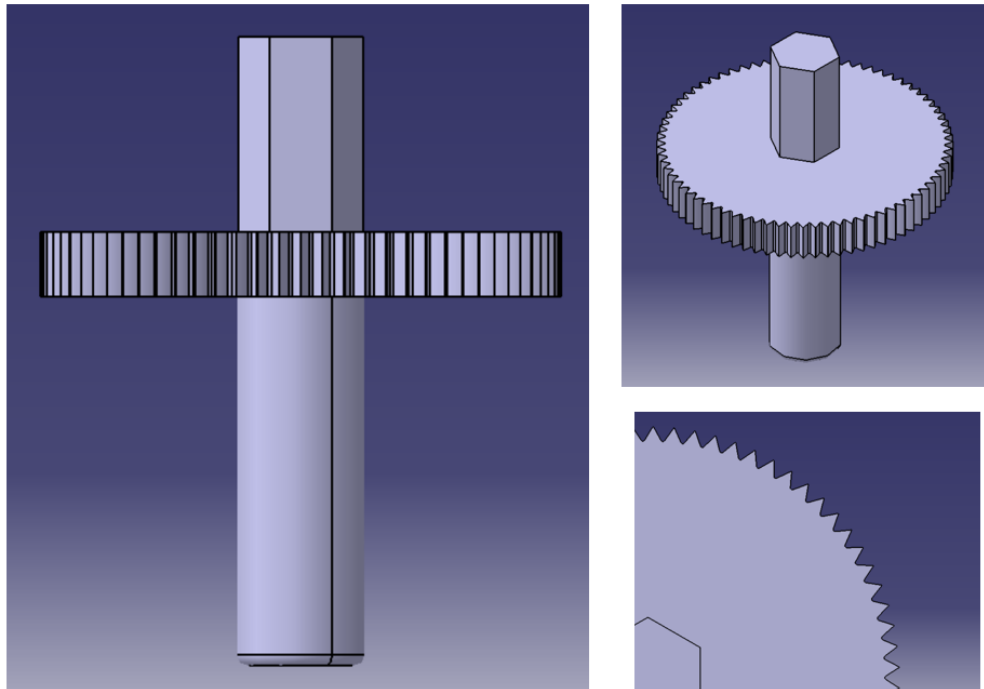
Engranaje reductor con eje hexagonal, realizado con CATIA V5
